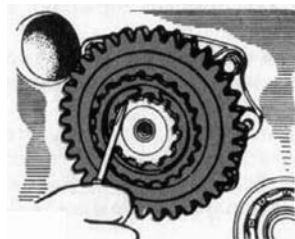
Снятие стопорного кольца и ведомой шестерни понижающего редуктора.
